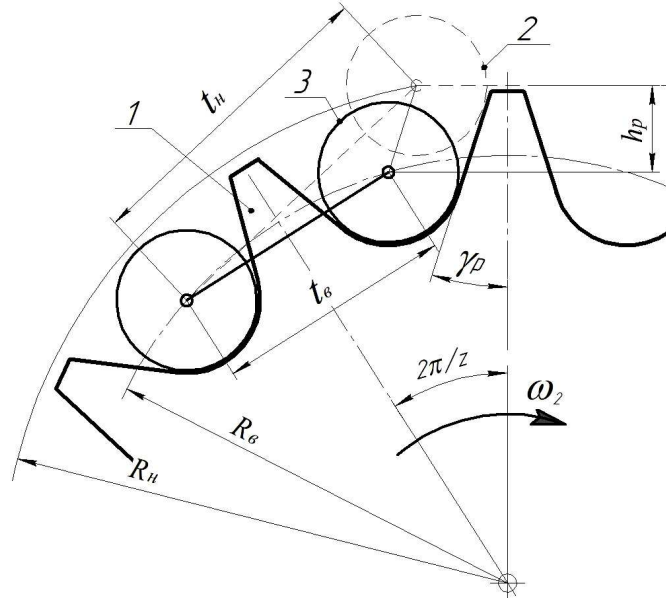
Схема для определения величины h_p для звездочки с симметричными зубьями
